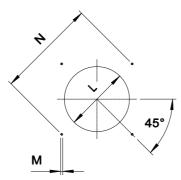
ФЛАНЕЦ ДЛЯ УСТАНОВКИ ГОРЕЛКИ
